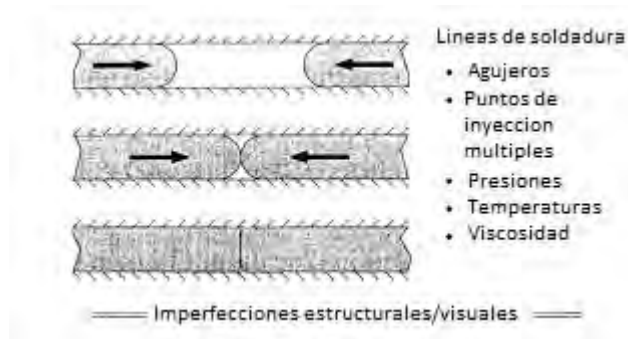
Formación de líneas de soldadura al unirse dos frentes [5].
